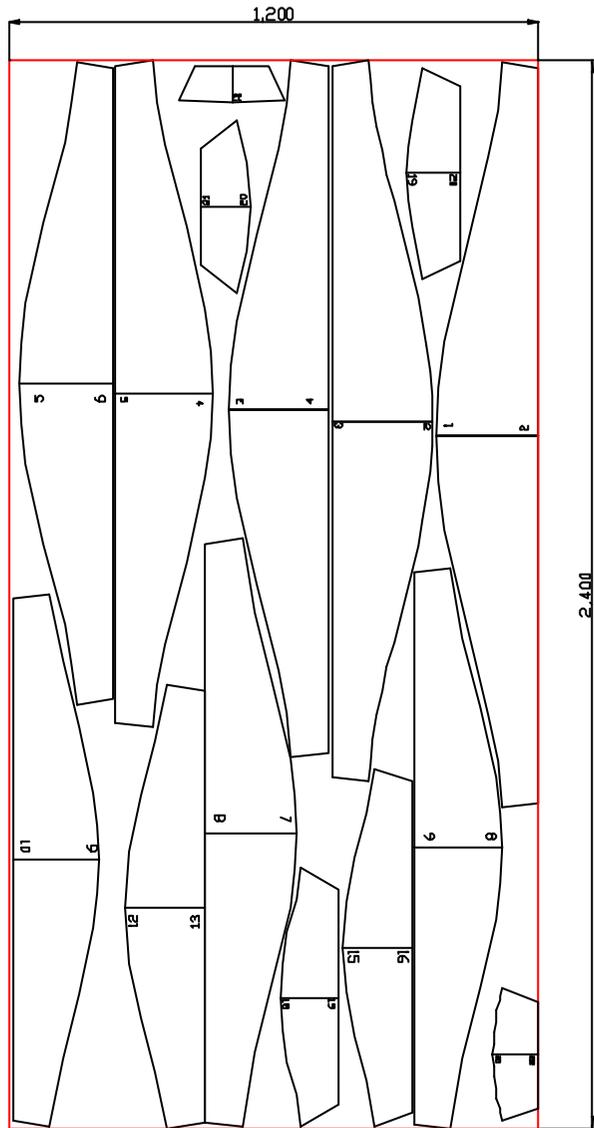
Ubicación de las plantillas de la espiral en la plancha de acero para el trazado y oxicorte (Segmentos indicados)
